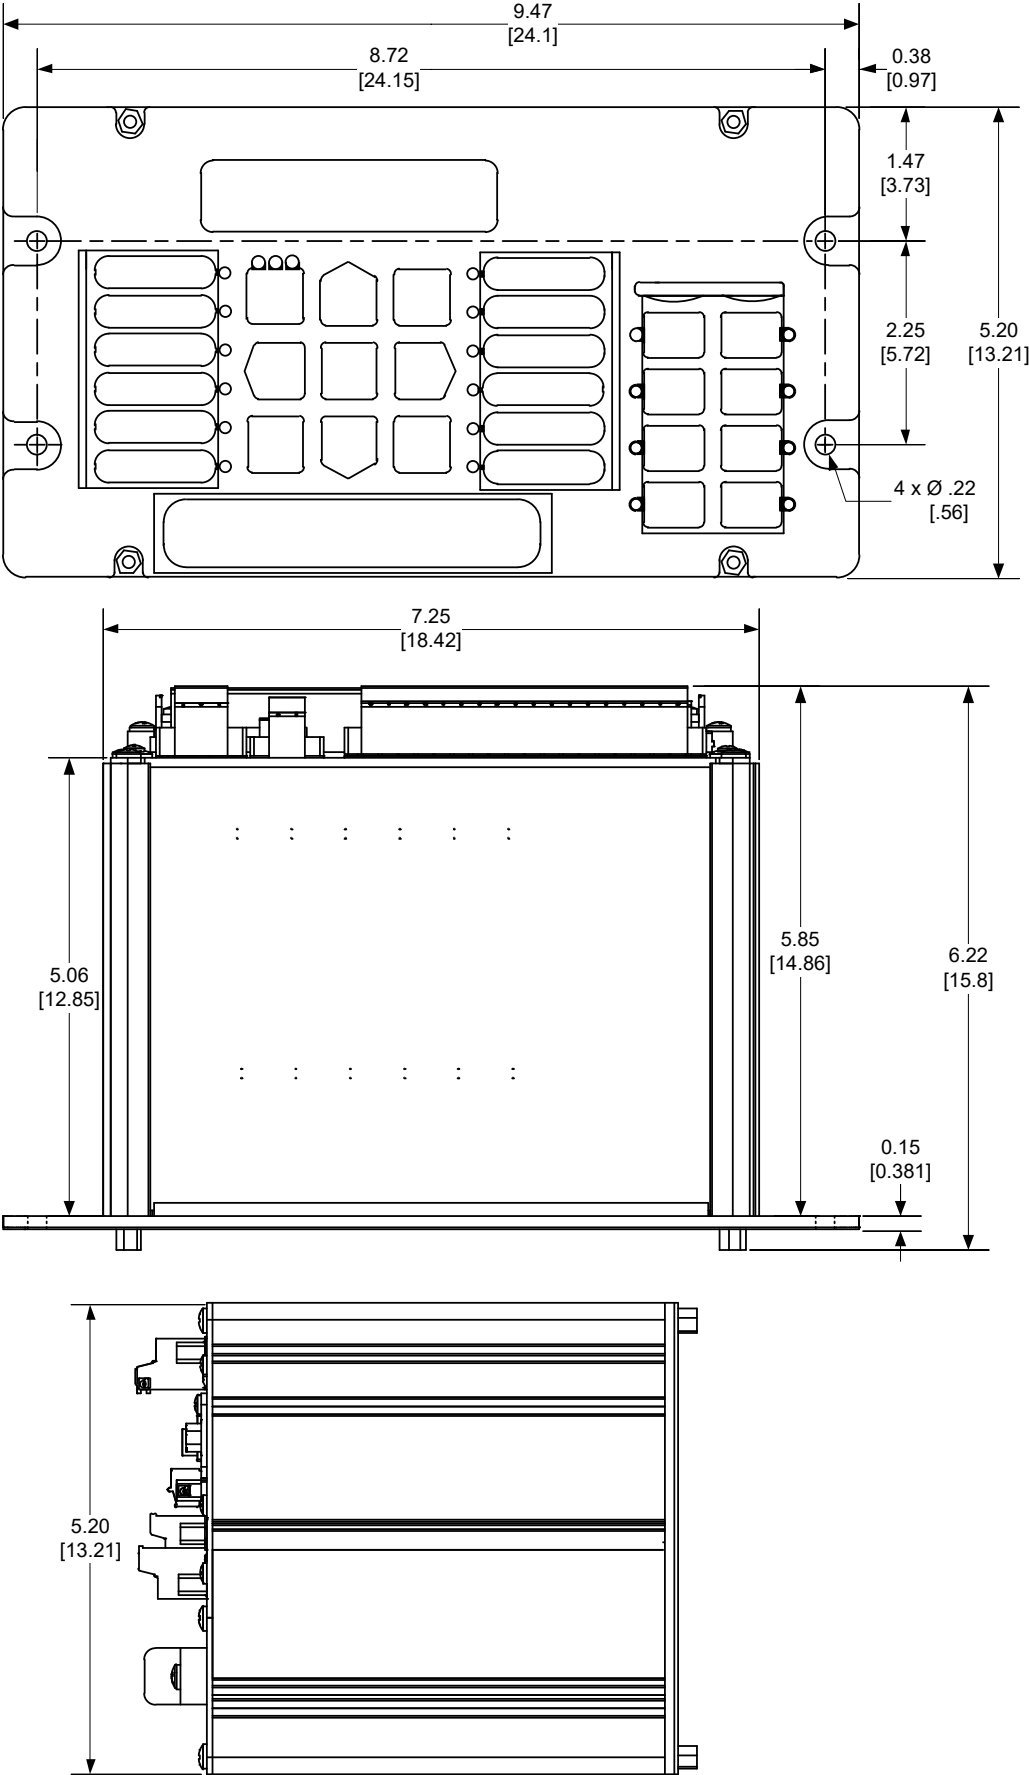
M-7679 Dimensiones de Montaje del Modelo Horizontal
